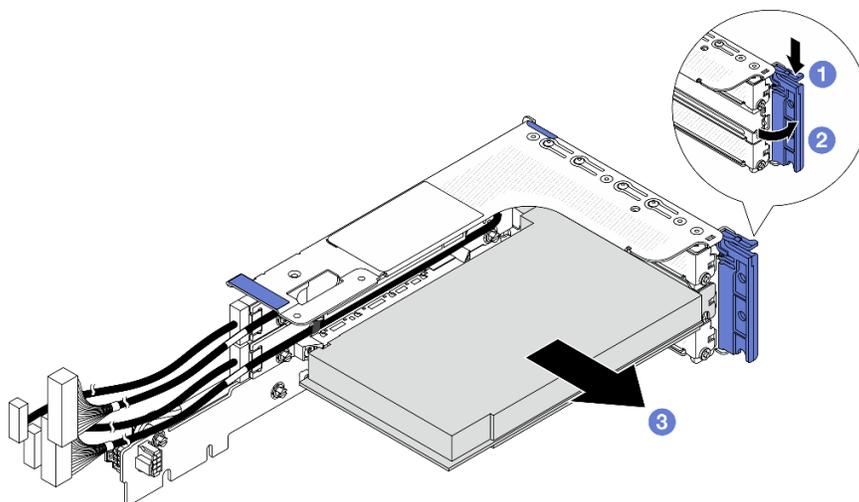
Remoção de um adaptador PCIe da gaiola da placa riser 3FH
